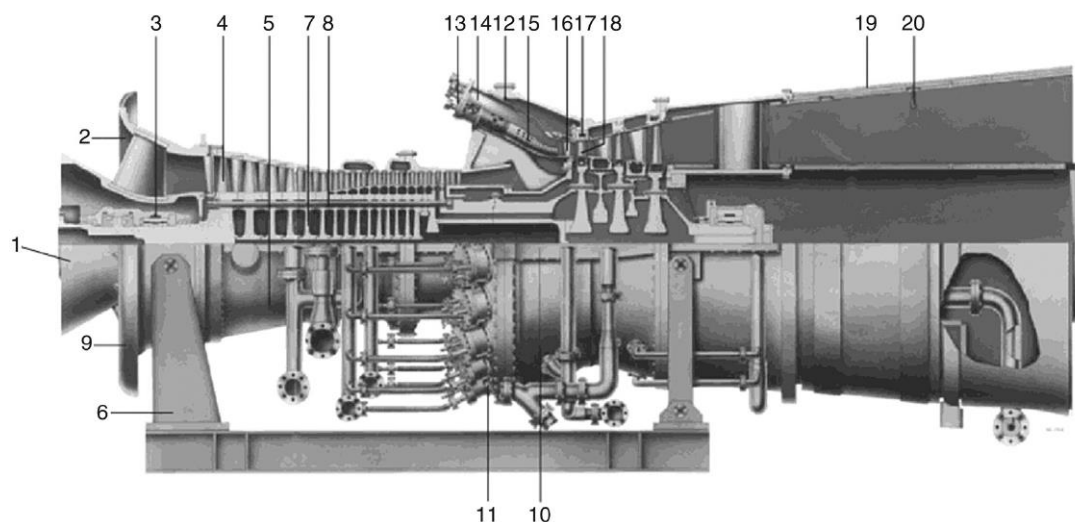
Estrutura de uma microturbina a gás [34] Legenda: 1 – Acoplamento de carga; 2 – Entrada de fluxo de ar radial/axial; 3 – Rolamento radial; 4 – Palheta do rotor do compressor; 5 – Estrutura do compressor; 6 – Suporte; 7 – Disco do compressor; 8 – Tirante; 9 – Câmara de entrada de ar; 10 – Câmara de combustão; 11 – Frente da câmara de combustão; 12 – Controlador de entrada do fluxo de combustível; 13 – Injetor de combustível; 14 – Tubo para a chama de ignição da câmara de combustão; 15 – Estrutura de refrigeração da câmara de combustão; 16 – Bocais; 17 – O-ring de proteção para as lâminas do rotor; 18 – Palheta do rotor da turbina; 19 – Difusor de escape; 20 – Termopar da câmara de saída de escape.
